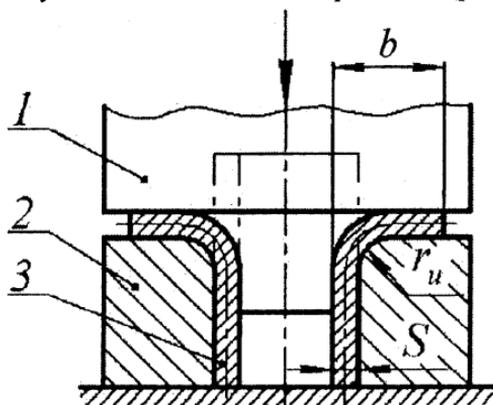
Схема раздачи трубной заготовки: 1 – пуансон; 2 – матрица; 3 – заготовка
